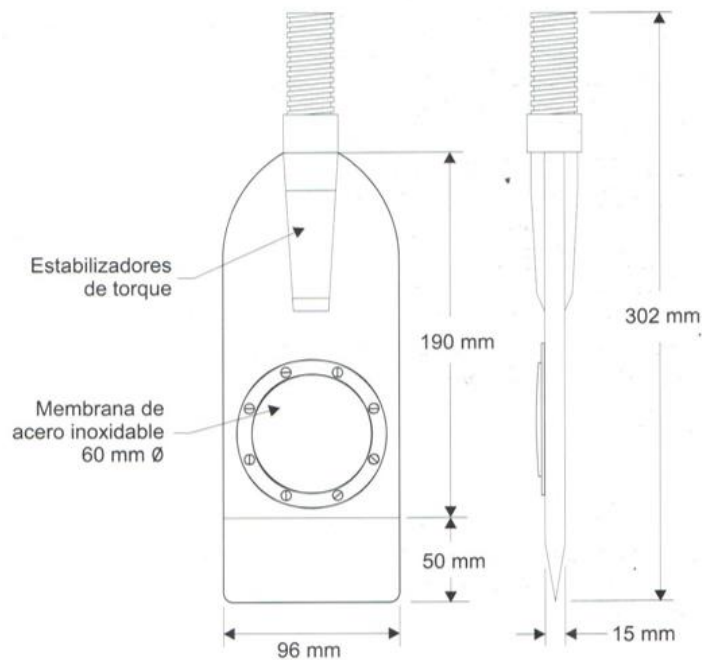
Componentes de equipo de Dilatómetro de Marchetti
